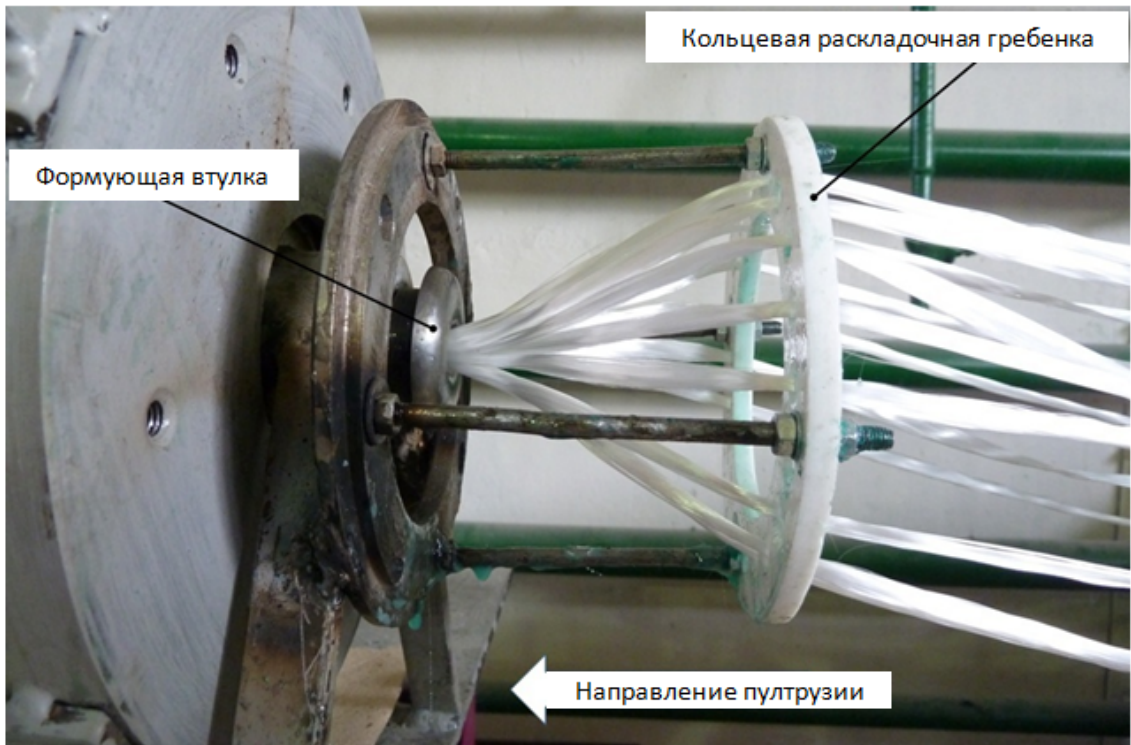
Внешний вид и конструкция формующей втулки (экспериментальный образец)
